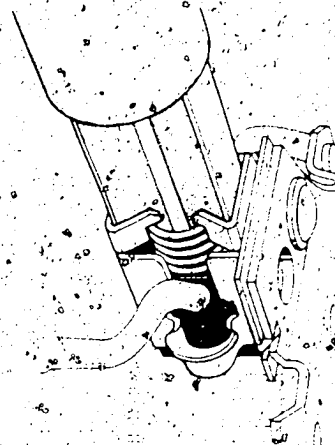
Umbiegen der Haltelappen mit Sonderwerkzeug
